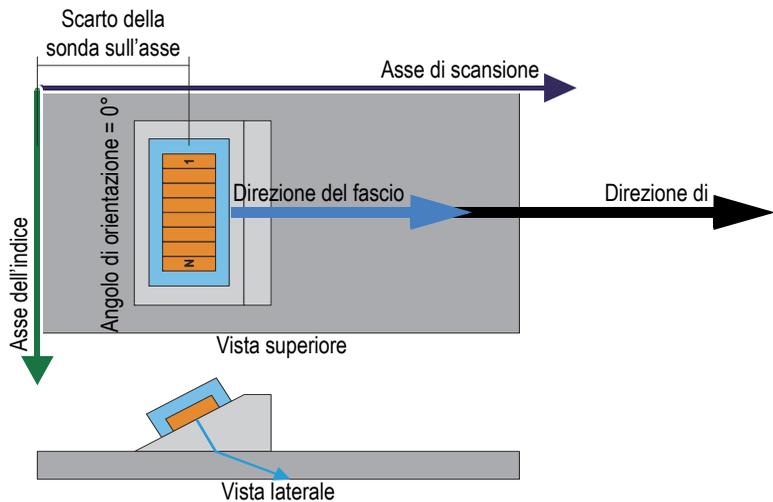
Ispezione di un rivetto con un angolo di orientazione da 0°
